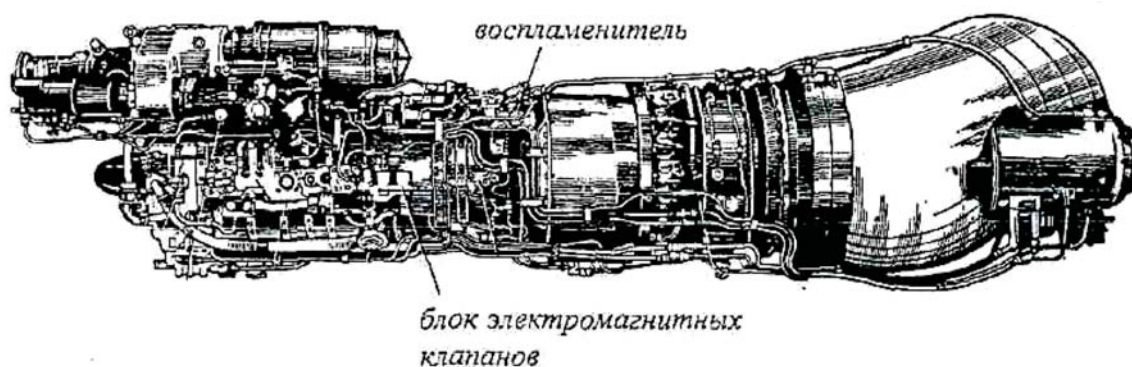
Внешний вид двигателя ТВ2-117А
